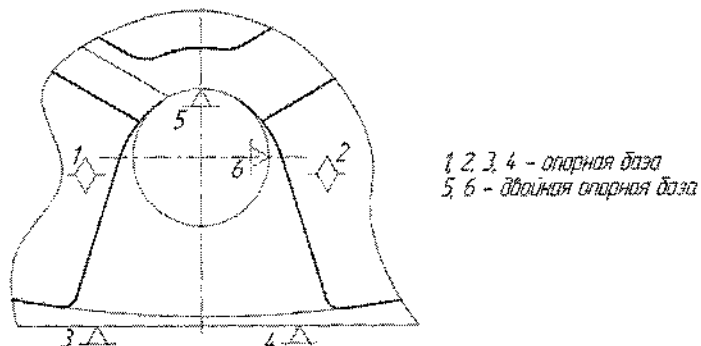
Схема базирования для фрезерной операции с ЧПУ
